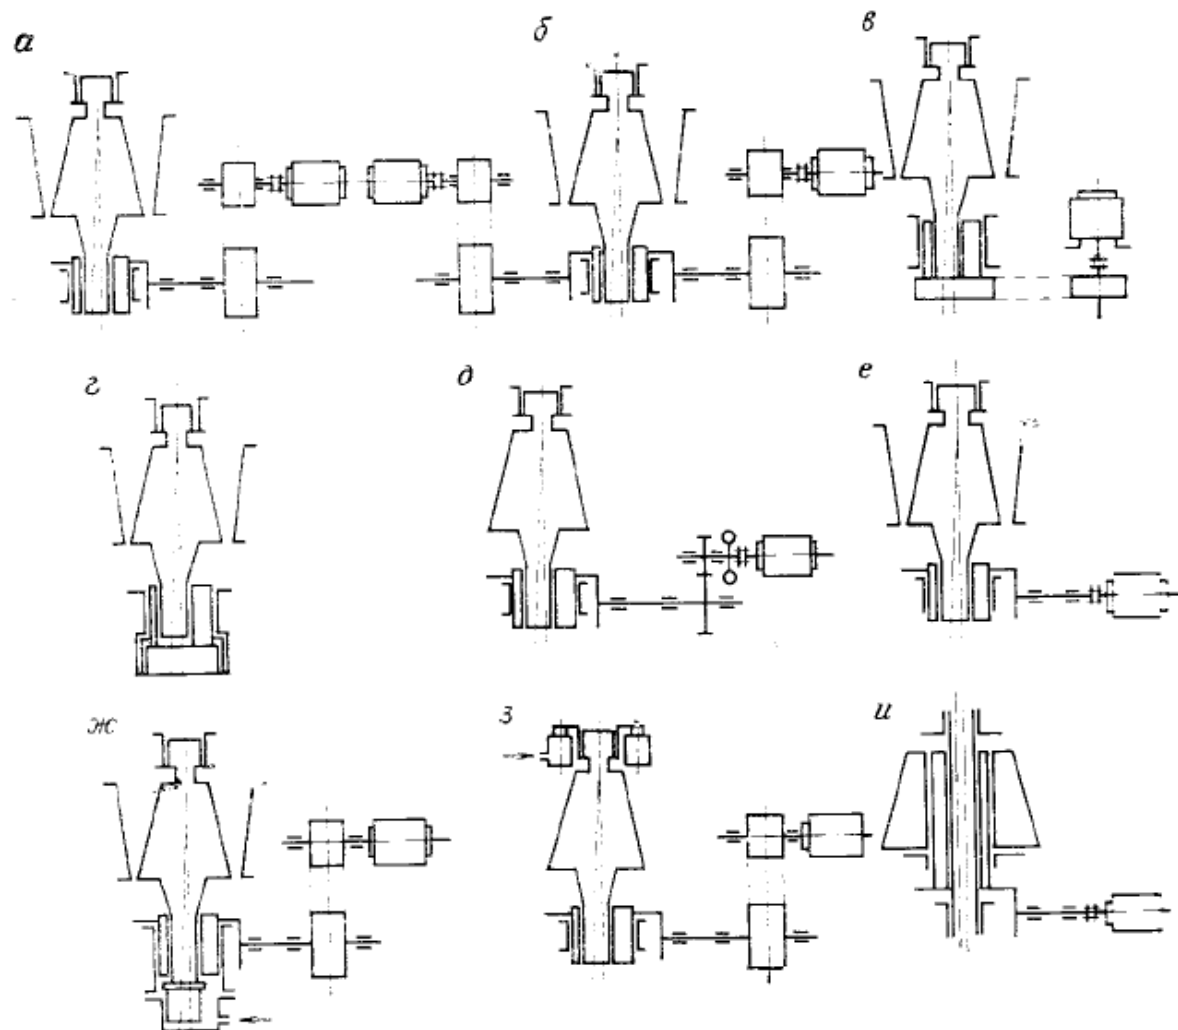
Кінематичні схеми конусних дробарок крупного дроблення:
